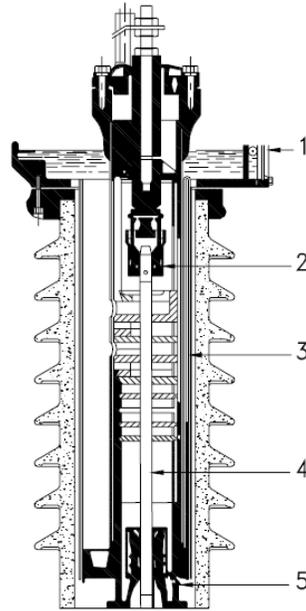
Cámara de soplo mixto. 1. Nivel de aceite, 2. Contacto deslizante superior (fijo), 3. Cubierta aislante, 4. Espiga de contacto móvil, 5. Contacto deslizante inferior (móvil).
